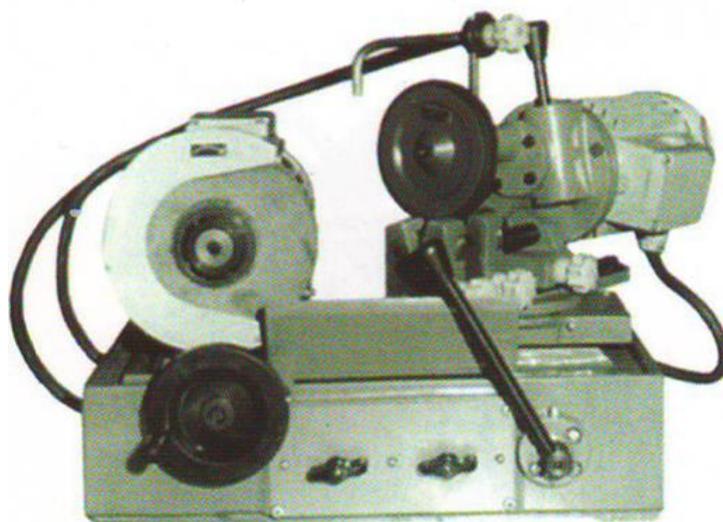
Станок для шлифовки фасок и торцов клапанов
